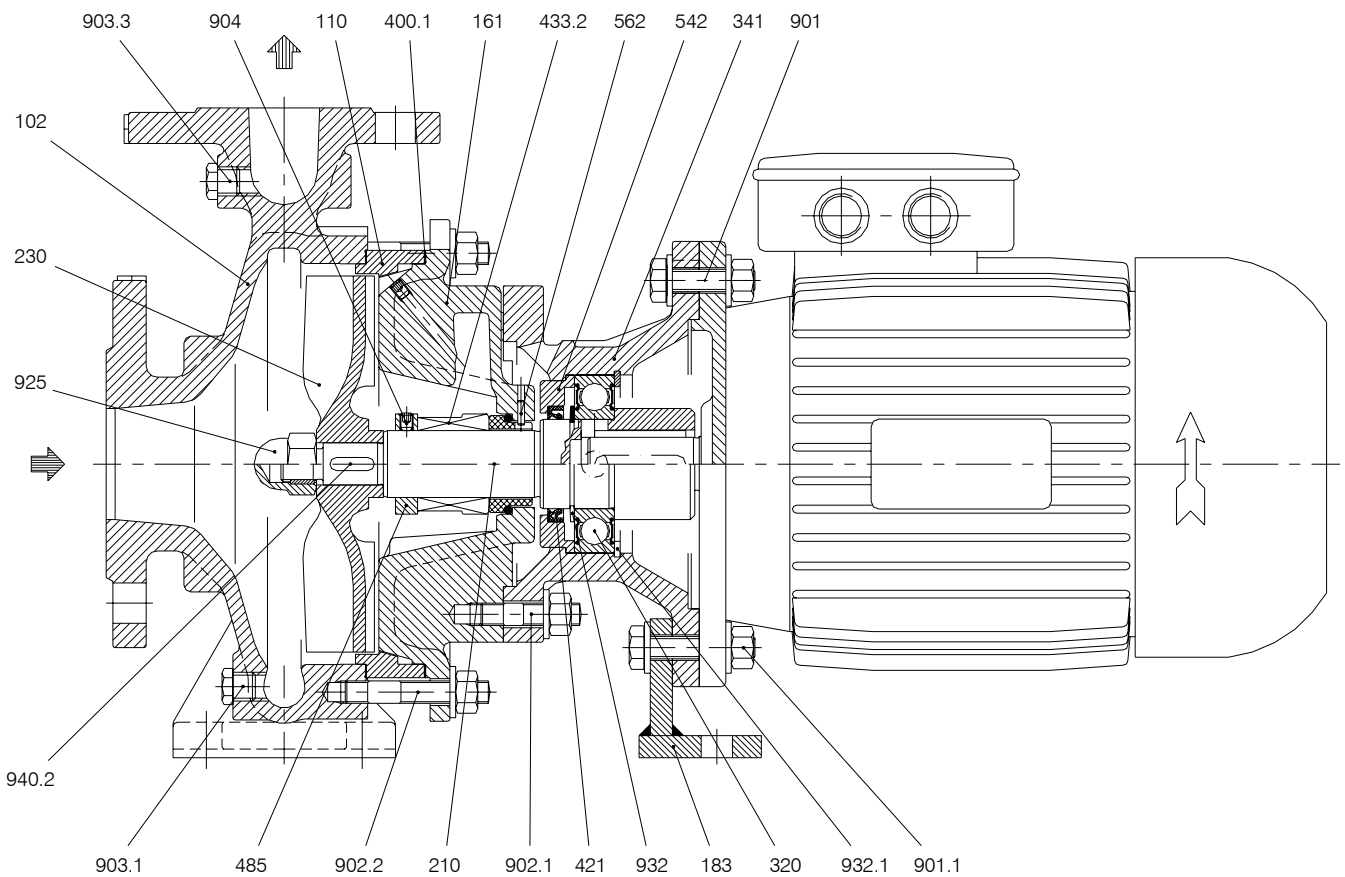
Bomba serie TCTM gr. 1 y 2 en ejecución /1-C = con cierre mecánico simple y motor tamaño 80 y 90
